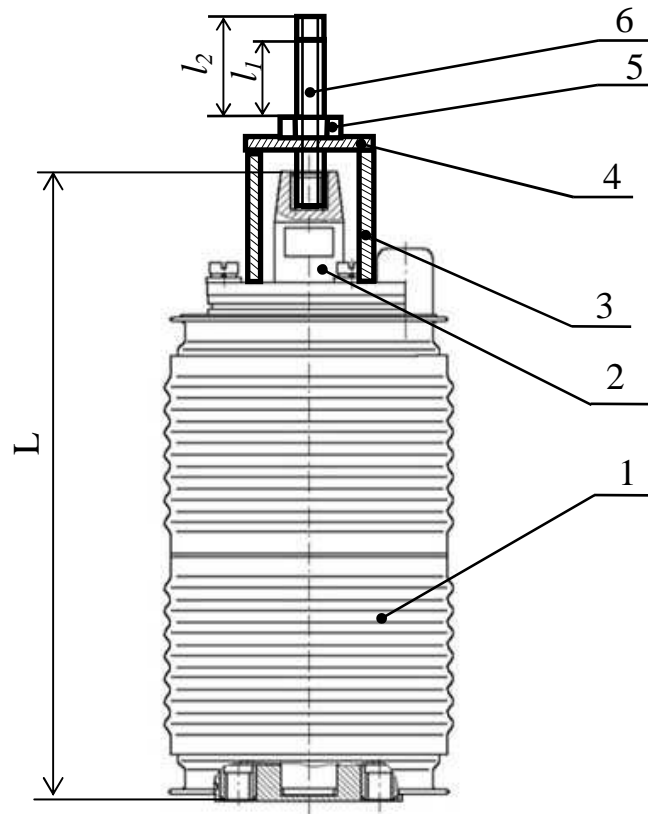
Габаритные, присоединительные и установочные размеры камеры типоразмера КДВ3-10-5/400 УХЛ2-2
